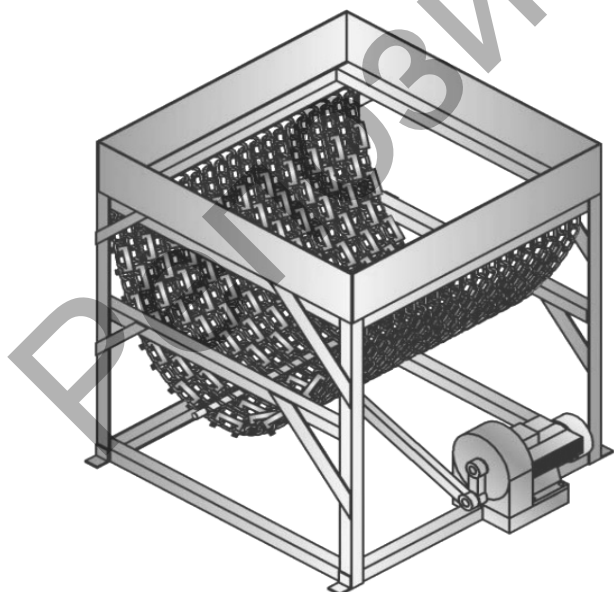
Цепной агрегат с одноволновой рабочей камерой и верхним подвесом маятниковых рычагов
